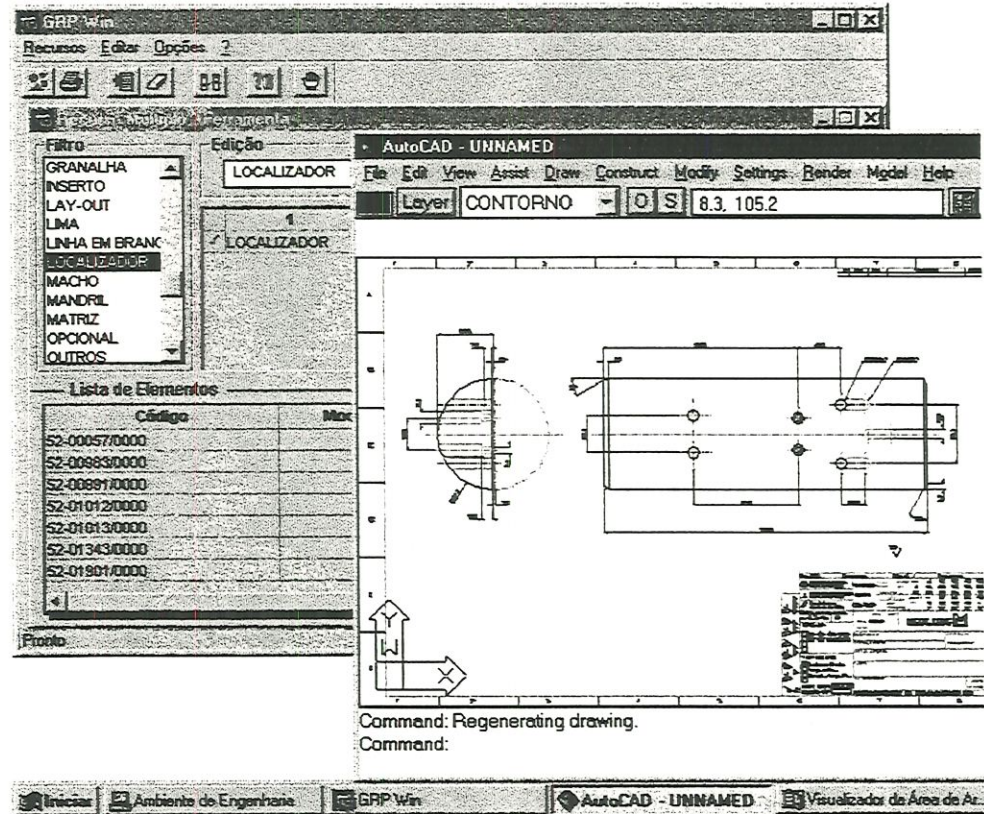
Desenho CAD executado automaticamente a partir do GRP.
